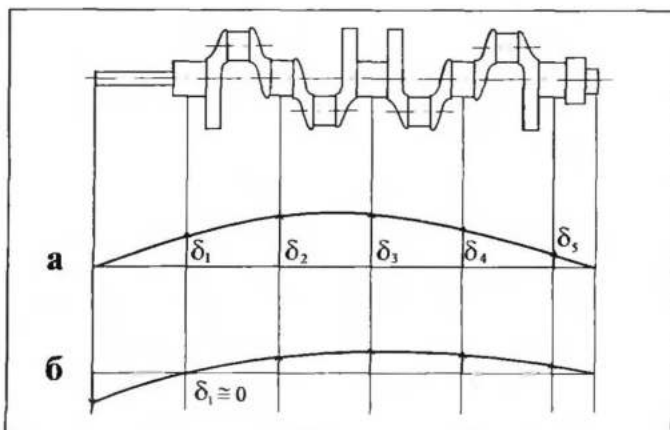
Уменьшение биения опорных шеек правкой центральной фаски хвостовика на минимум биения первой опорной шейки: а — до правки фаски; б — после правки фаски биения опорных шеек малы, но требуется наварка и шлифовка хвостовика
